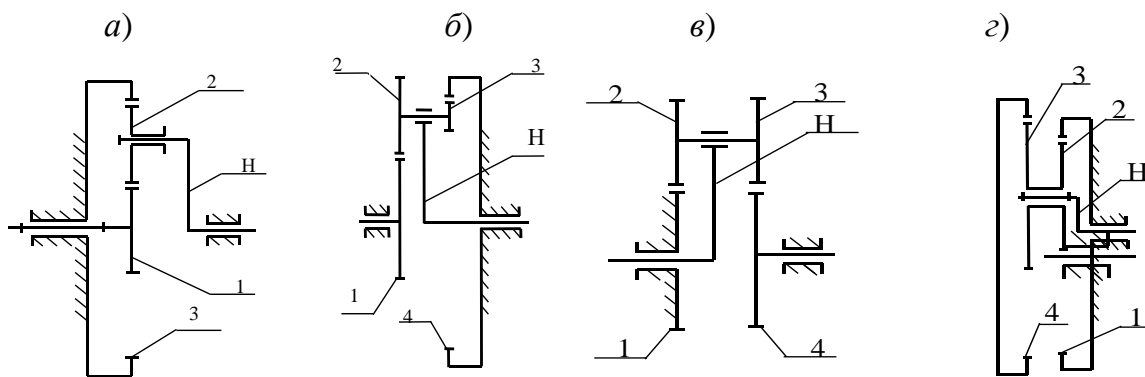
Схемы планетарных зубчатых механизмов: а) механизм Джеймса; б) механизм со сдвоенными сателлитами; в) механизм Давида; г) механизм со сдвоенными сателлитами и двумя внутренними зацеплениями
